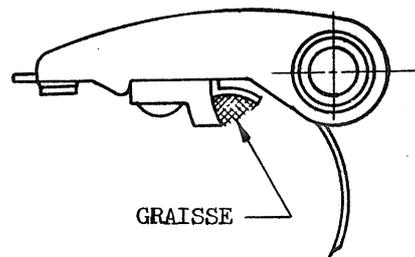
ENDROIT OU IL FAUT METTRE DE LA GRAISSE SUR LE LINGUET POUR GRAISSER LA PLAQUETTE DE FRICTION.
